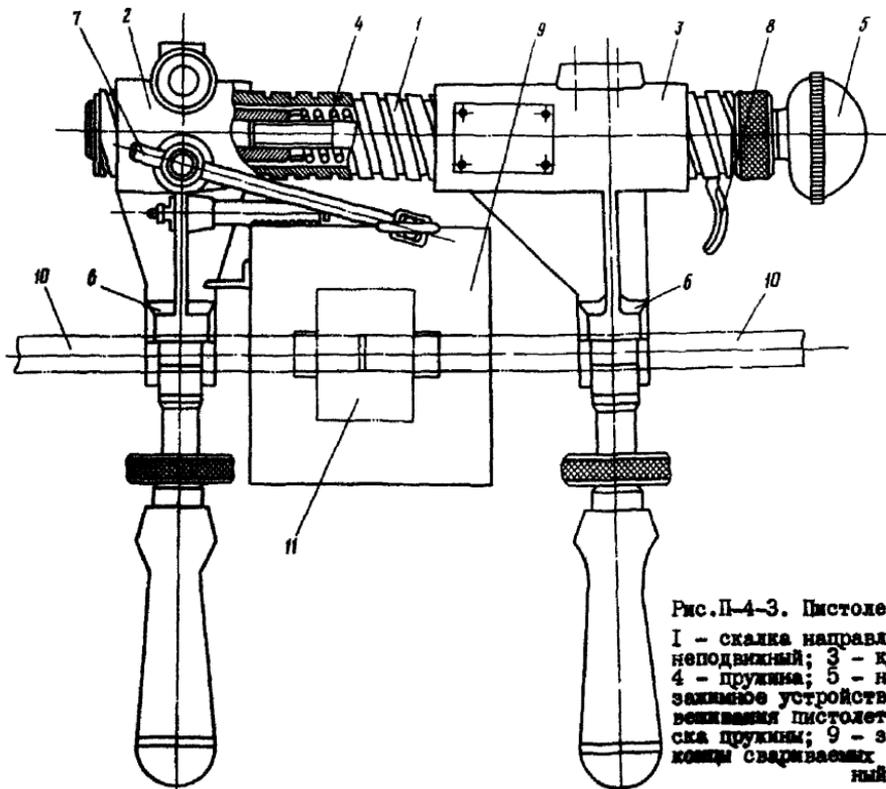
Пистолет для сварки проводов:
